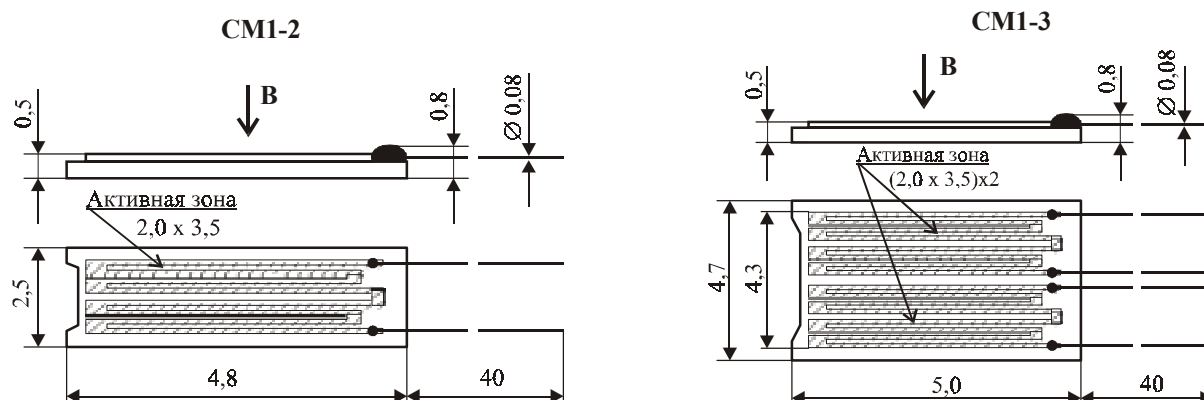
Внешний вид и габаритные размеры магниторезисторов CM1-2 и CM1-3
